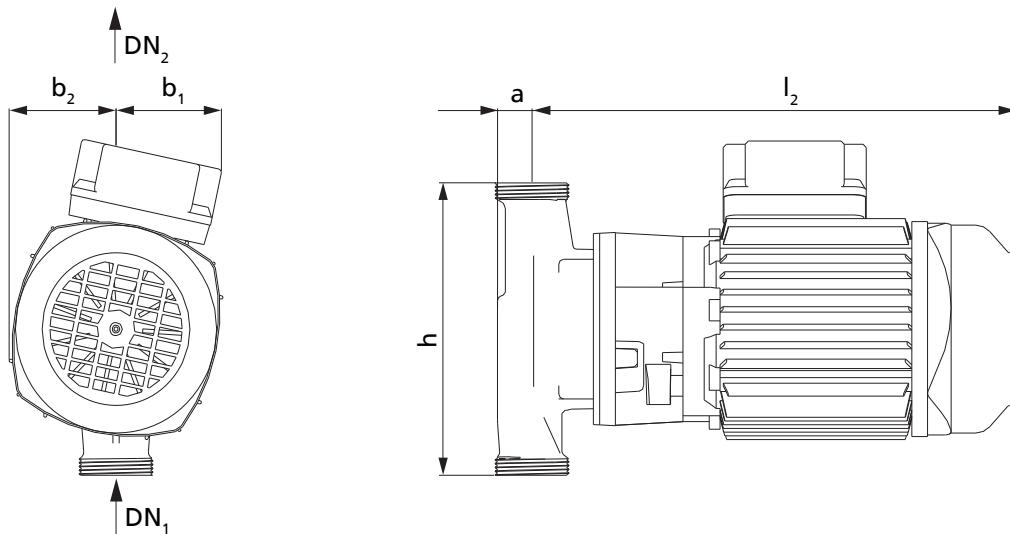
Dimensiones del grupo motobomba con conexión roscada, tamaño < 032-032-100
